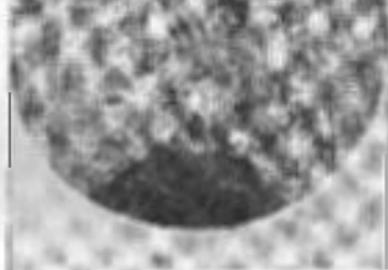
Газовая пора и микротрещина при сварке чугуна модель-металлом, когда газовая пора определила направление микротрещины. Шлиф травлен, увеличение в 100 раз
